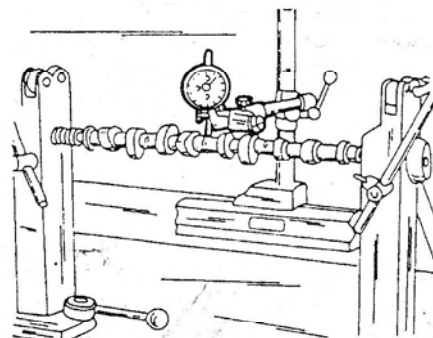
Контроль биения распределительного вала в центрах токарного станка.
